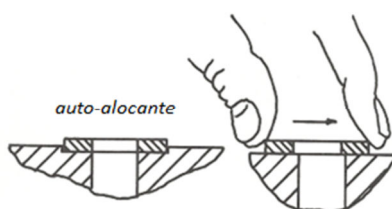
Componente difícil de posicionar e geometria alternativa do conjunto [adaptado de [7]]
